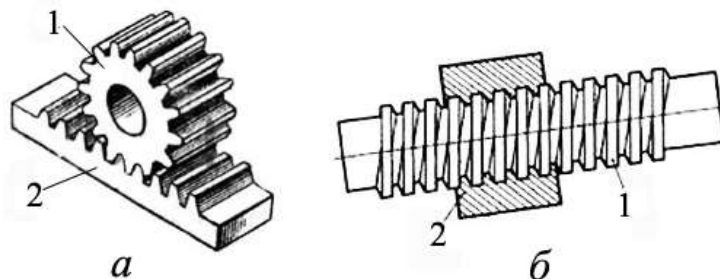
Рейкова (*а*) і передача гвинт-гайка (*б*)
